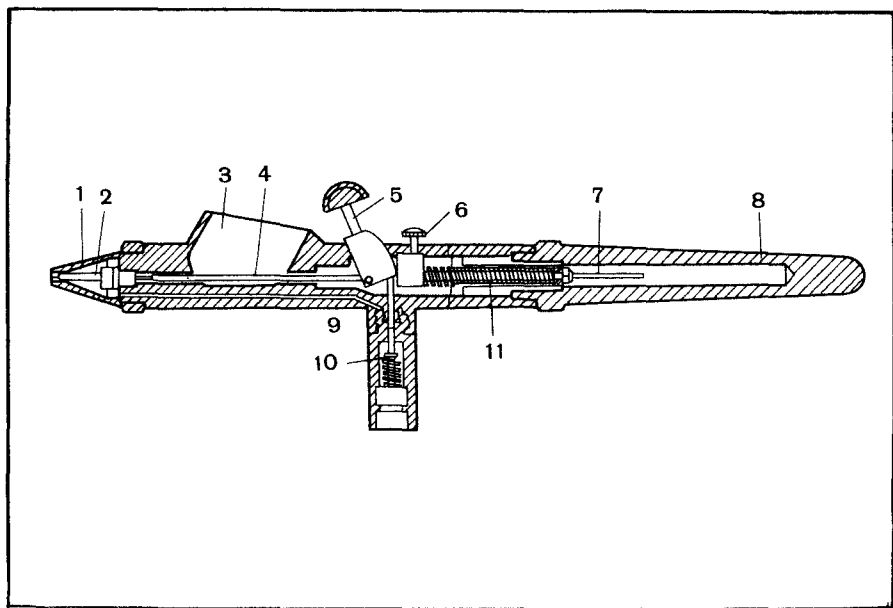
Устройство аэрографа: 1 — защитный кожух сопла; 2 — сопло; 3 — резервуар для краски; 4 — игла; 5 — рычаг клапана; 6 — фиксатор положения иглы; 7 — игла; 8 — защитный кожух; 9 — отверстие для подвода воздуха; 10 — клапан; 11 — пружина для подачи иглы вперед
